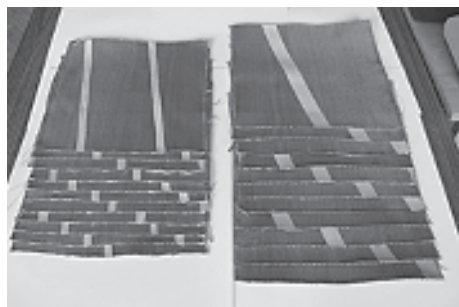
Заготовки для формования арамидного слоисто-тканого материала
